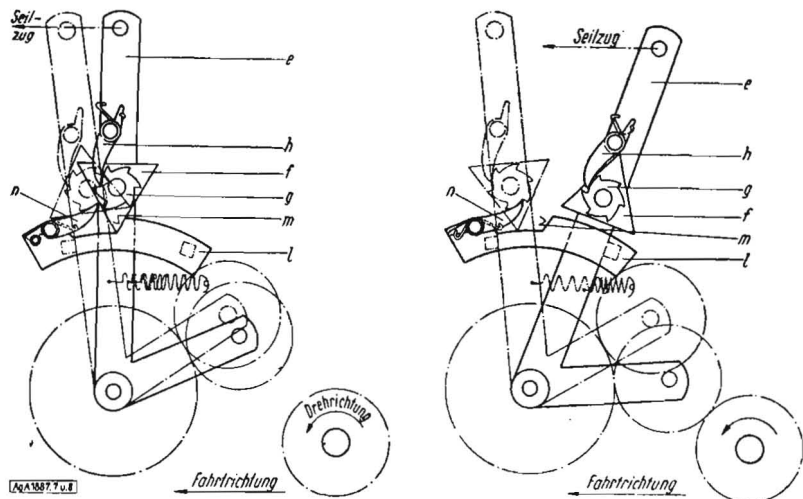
Ein- und Ausschaltvorrichtung für Drillmaschinen im ausgerückten Zustand
